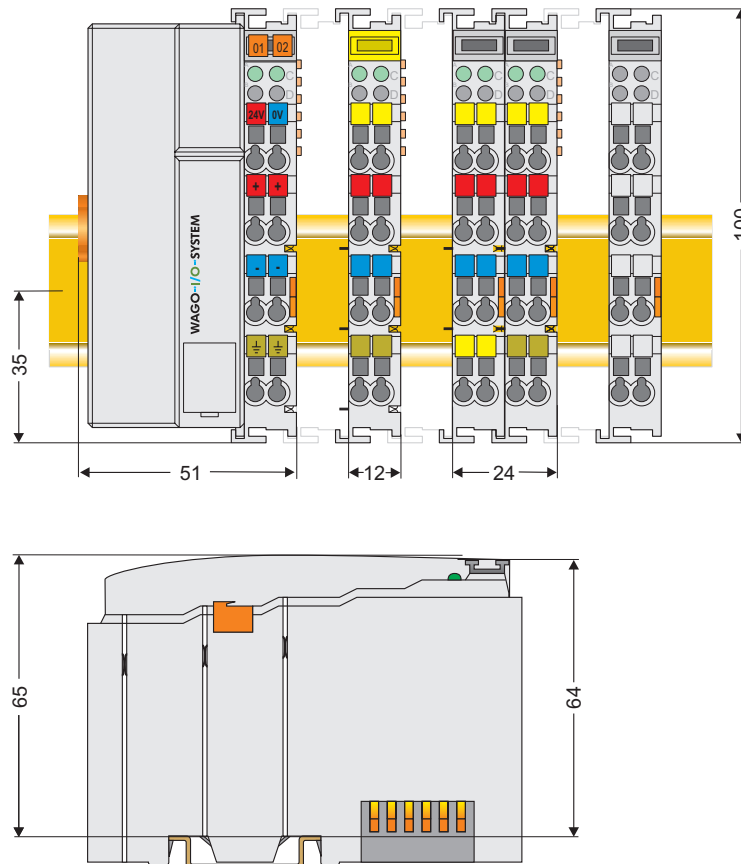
Габаритные размеры стандартного узла полевой шины
